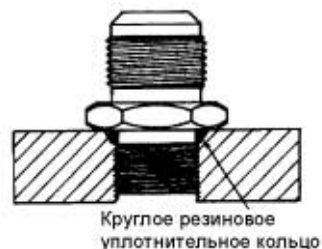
Штуцер с цилиндрической резьбой и круглым резиновым уплотнительным кольцом
